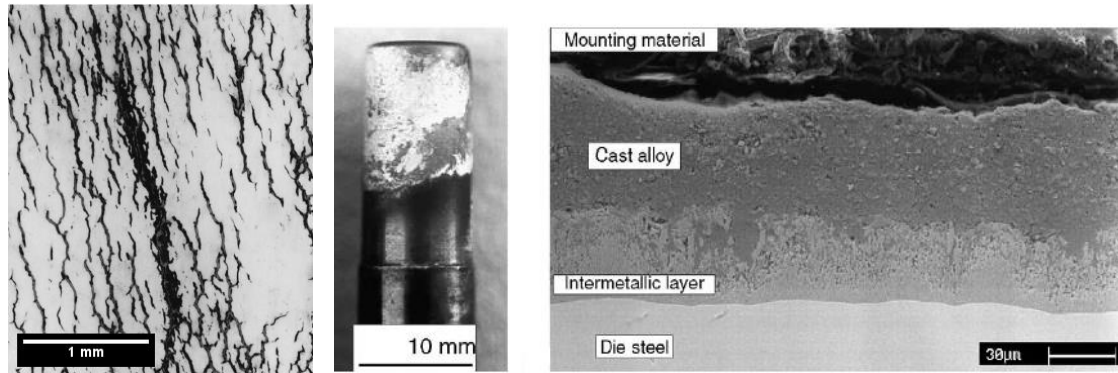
Defectos en moldes. a. Heat check [17]. b. Die soldering [18]
